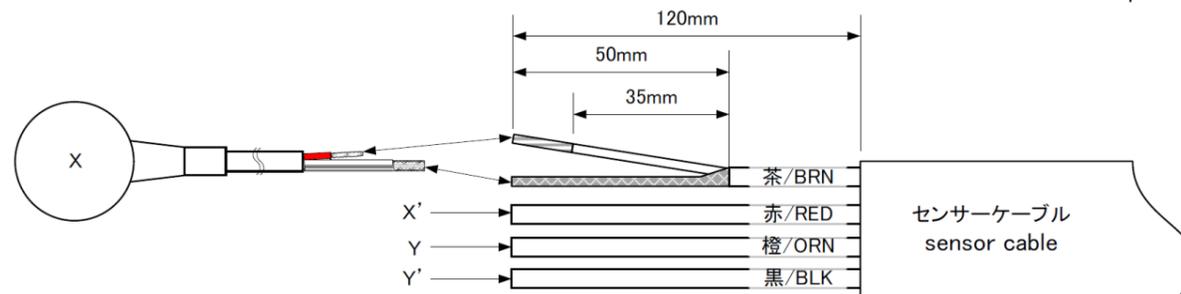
センサーケーブル端末加工図と接続/FIG. 3. Sensor cable terminal processing drawing and connection
